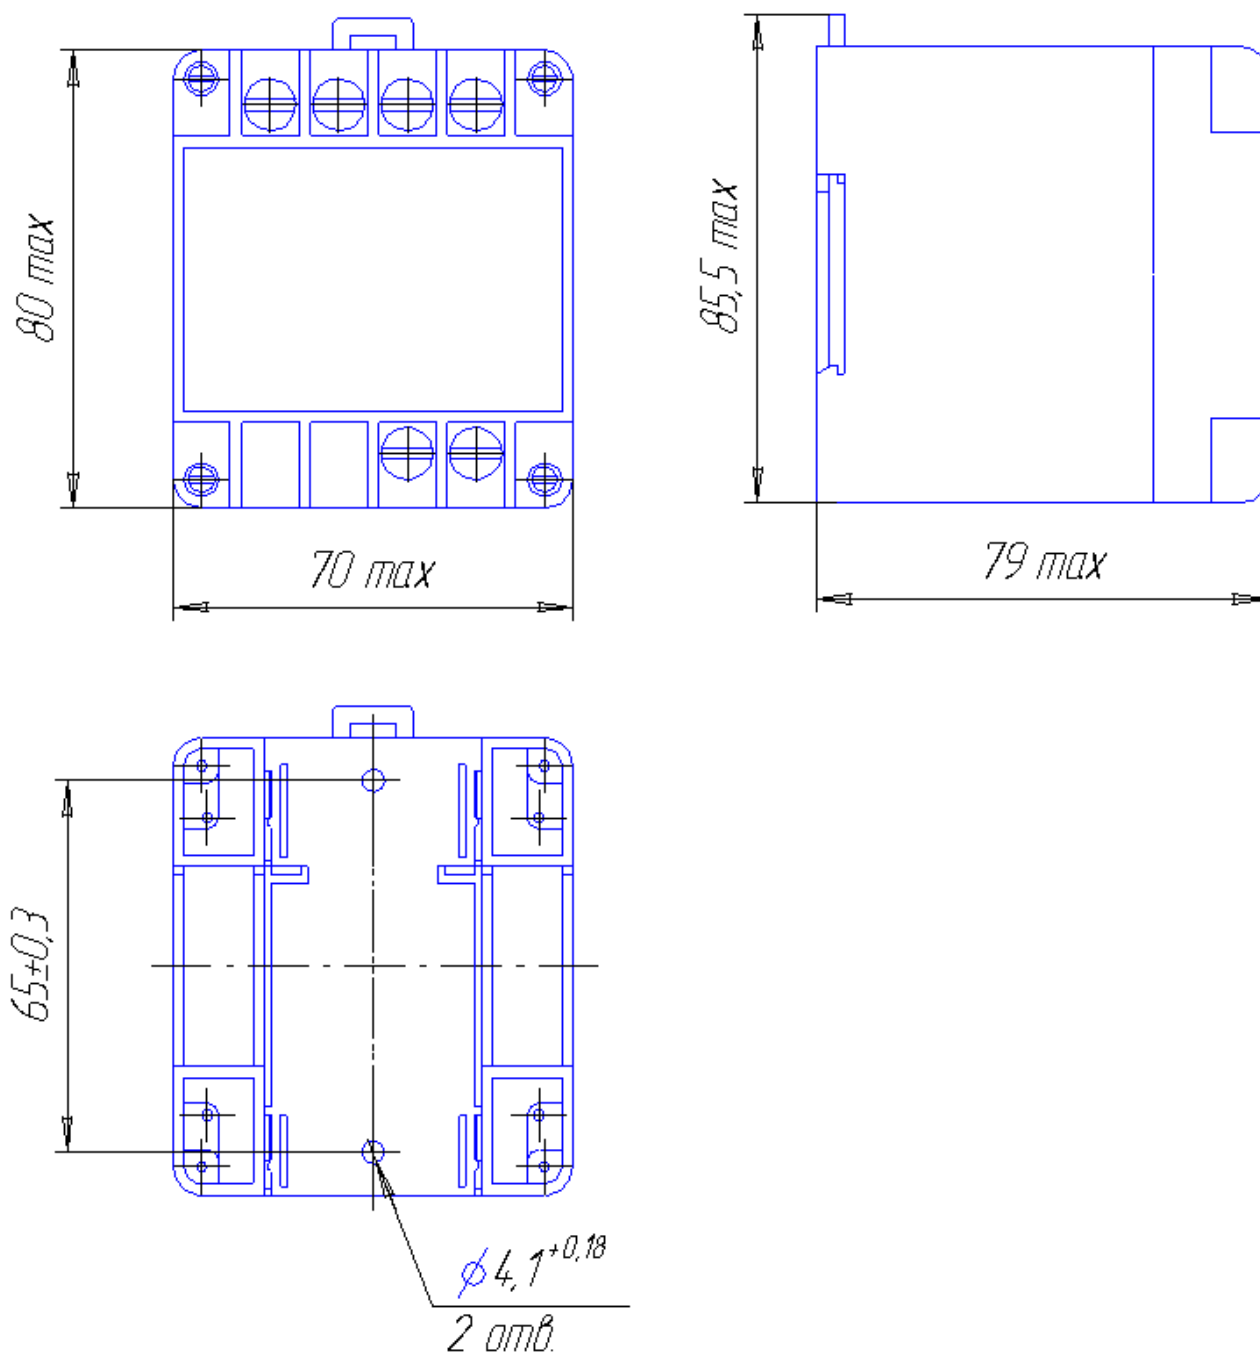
Общий вид, габаритные и установочные размеры преобразователей переменного тока и напряжения ЕП34Д.
